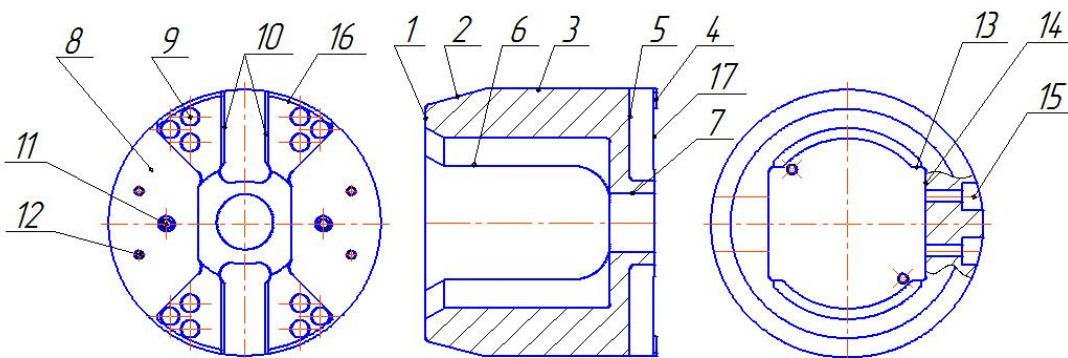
Поверхні деталі «Муфта П6-ВА4-А.15.09»
